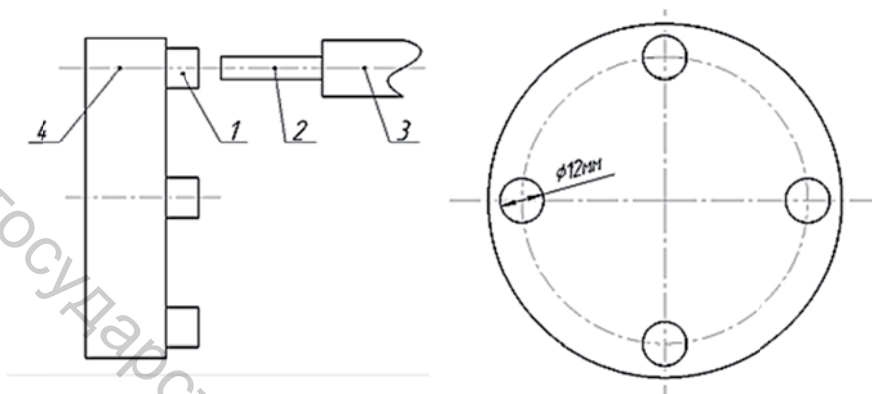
Шлифовальный круг в сборе (1 – абразивная головка; 2 – заготовка; 3 – устество крепления заготовки; 4 – шлифовальный круг)
